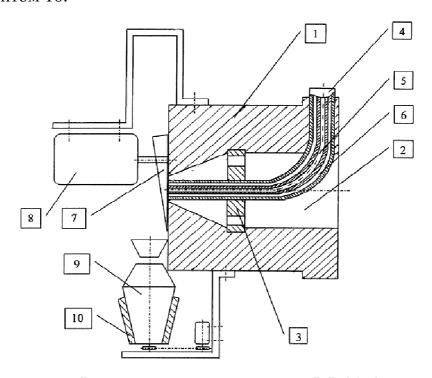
Формующий узел по патенту РФ 21726977 [12]: 1 – корпус; 2 – канал; 3 – решетчатая шайба; 4 – питающий канал; 5 – внутренняя трубка; 6 – внешняя трубка; 7 – механизм резки; 8 – привод; 9
